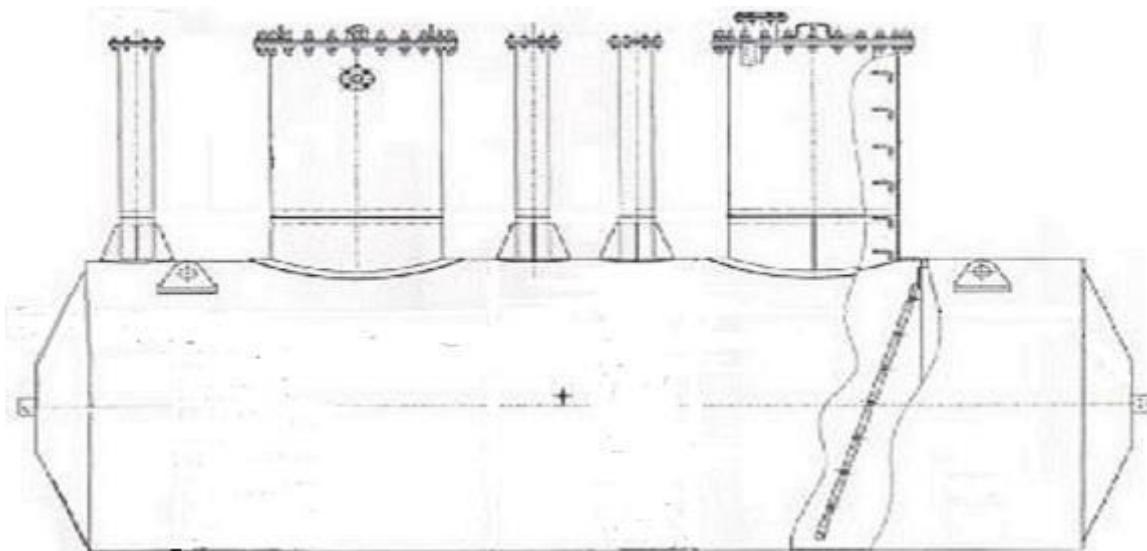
Эскиз общего вида резервуара горизонтального стального РГС-40-2400-1600-А-СО-У1
